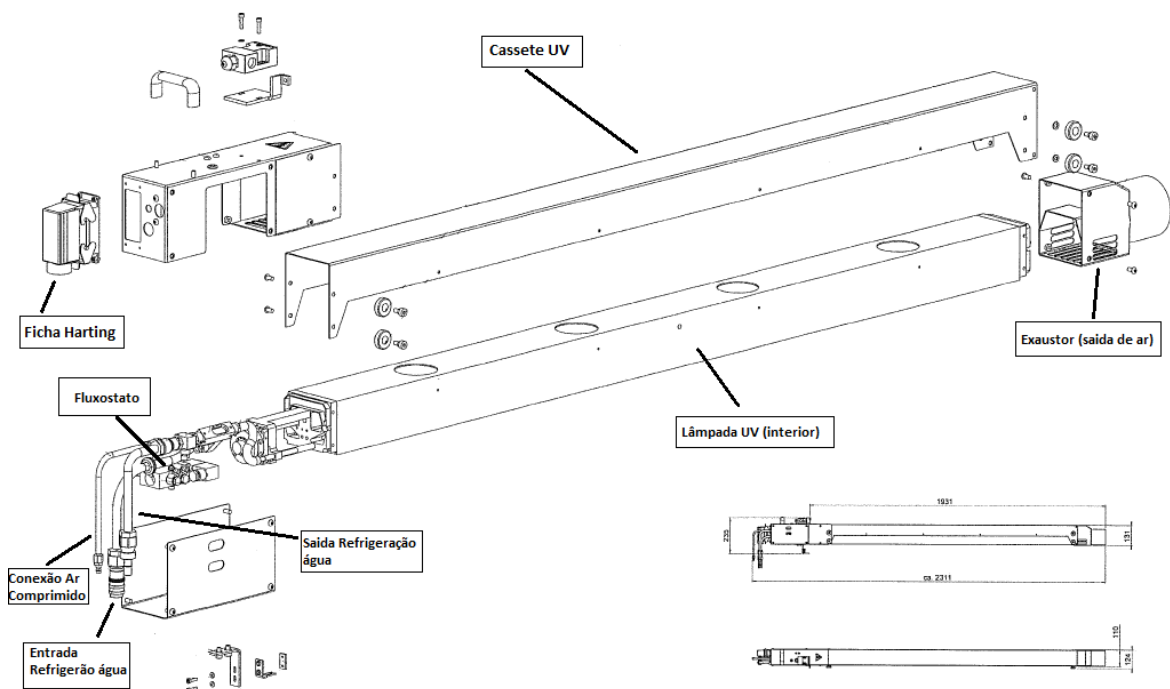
27- Desenho técnico do módulo UV da cassette de secagem
